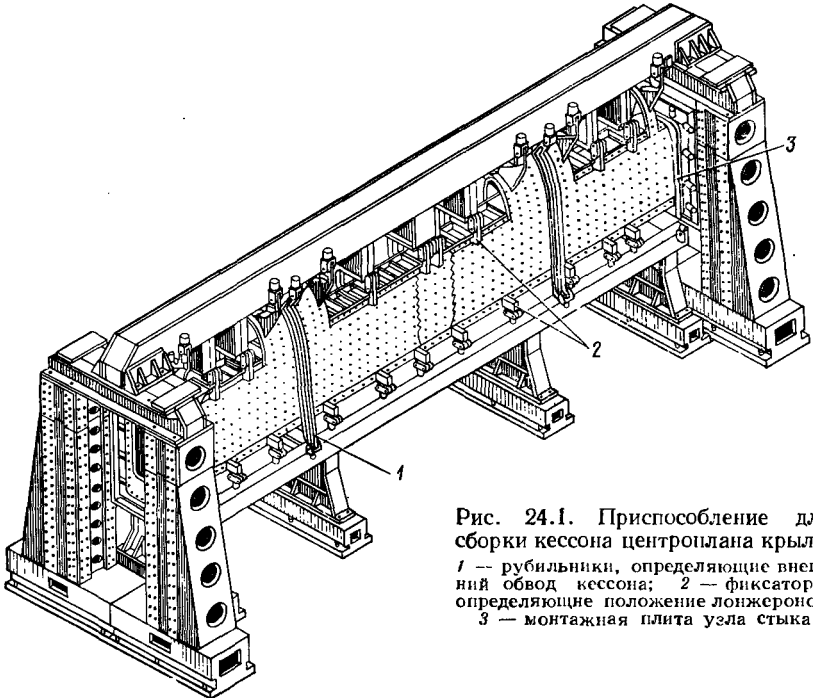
Приспособление для сборки кессона центроплана крыла:
